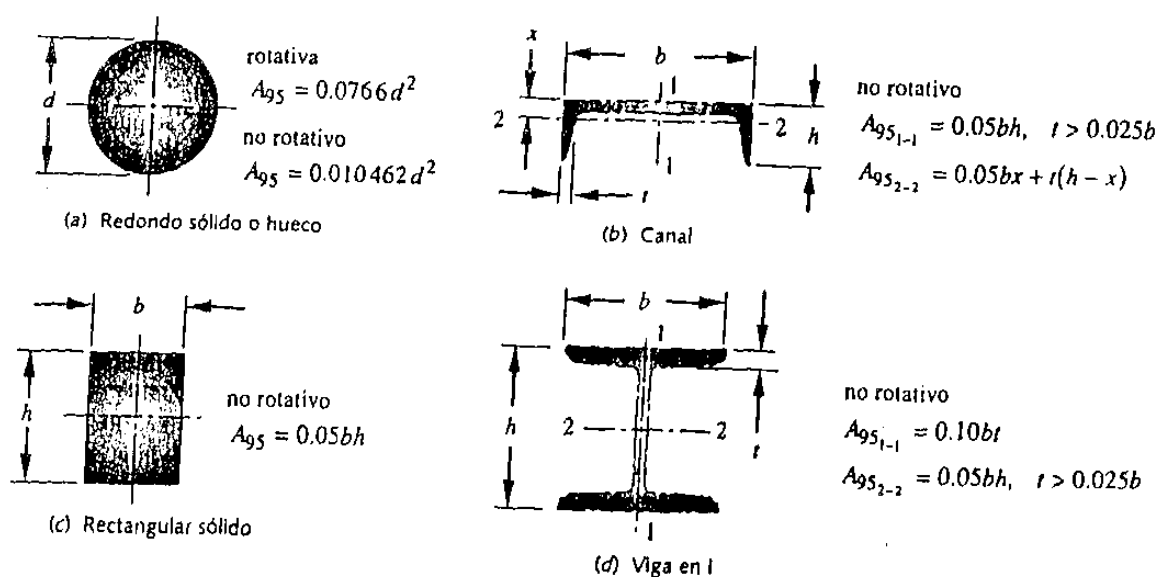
barra redonda maciza o hueca; b) canal; c) barra de sección rectangular; d) viga I de patín ancho. Fórmulas para áreas esforzadas al 95% de diversas secciones, cargadas a flexión.
